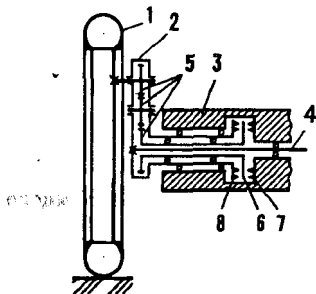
Кинематическая схема колесно-шагающего механизма с жесткой блокировкой: 1 — колесо; 2 — рычаг шагания; 3 — корпус машины; 4 — выходной вал тягового привода; 5 — редуктор; 6 — центральный диск муфты блокирующего механизма; 7 — полумуфта шагающего режима; 8 — полумуфта колесного режима
